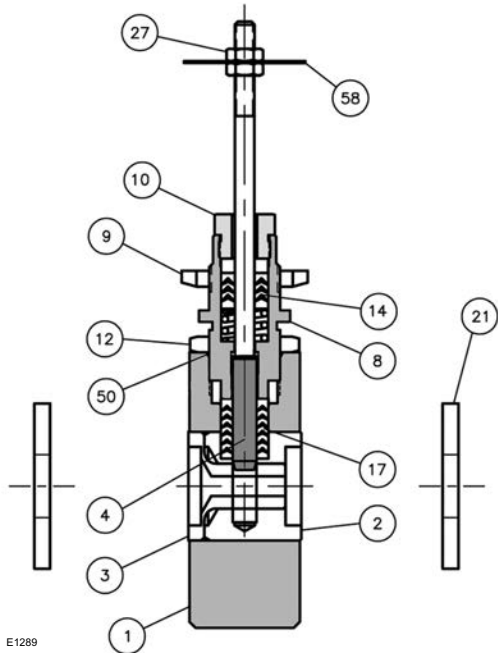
Корпус клапана для $Cv=4,2$ (Утечка из седла класса IV)
